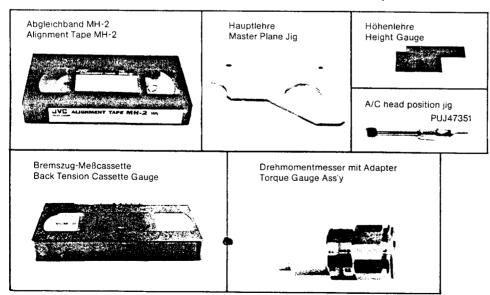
Lehren und Werkzeuge Fig. 1-3 Jigs and tools
